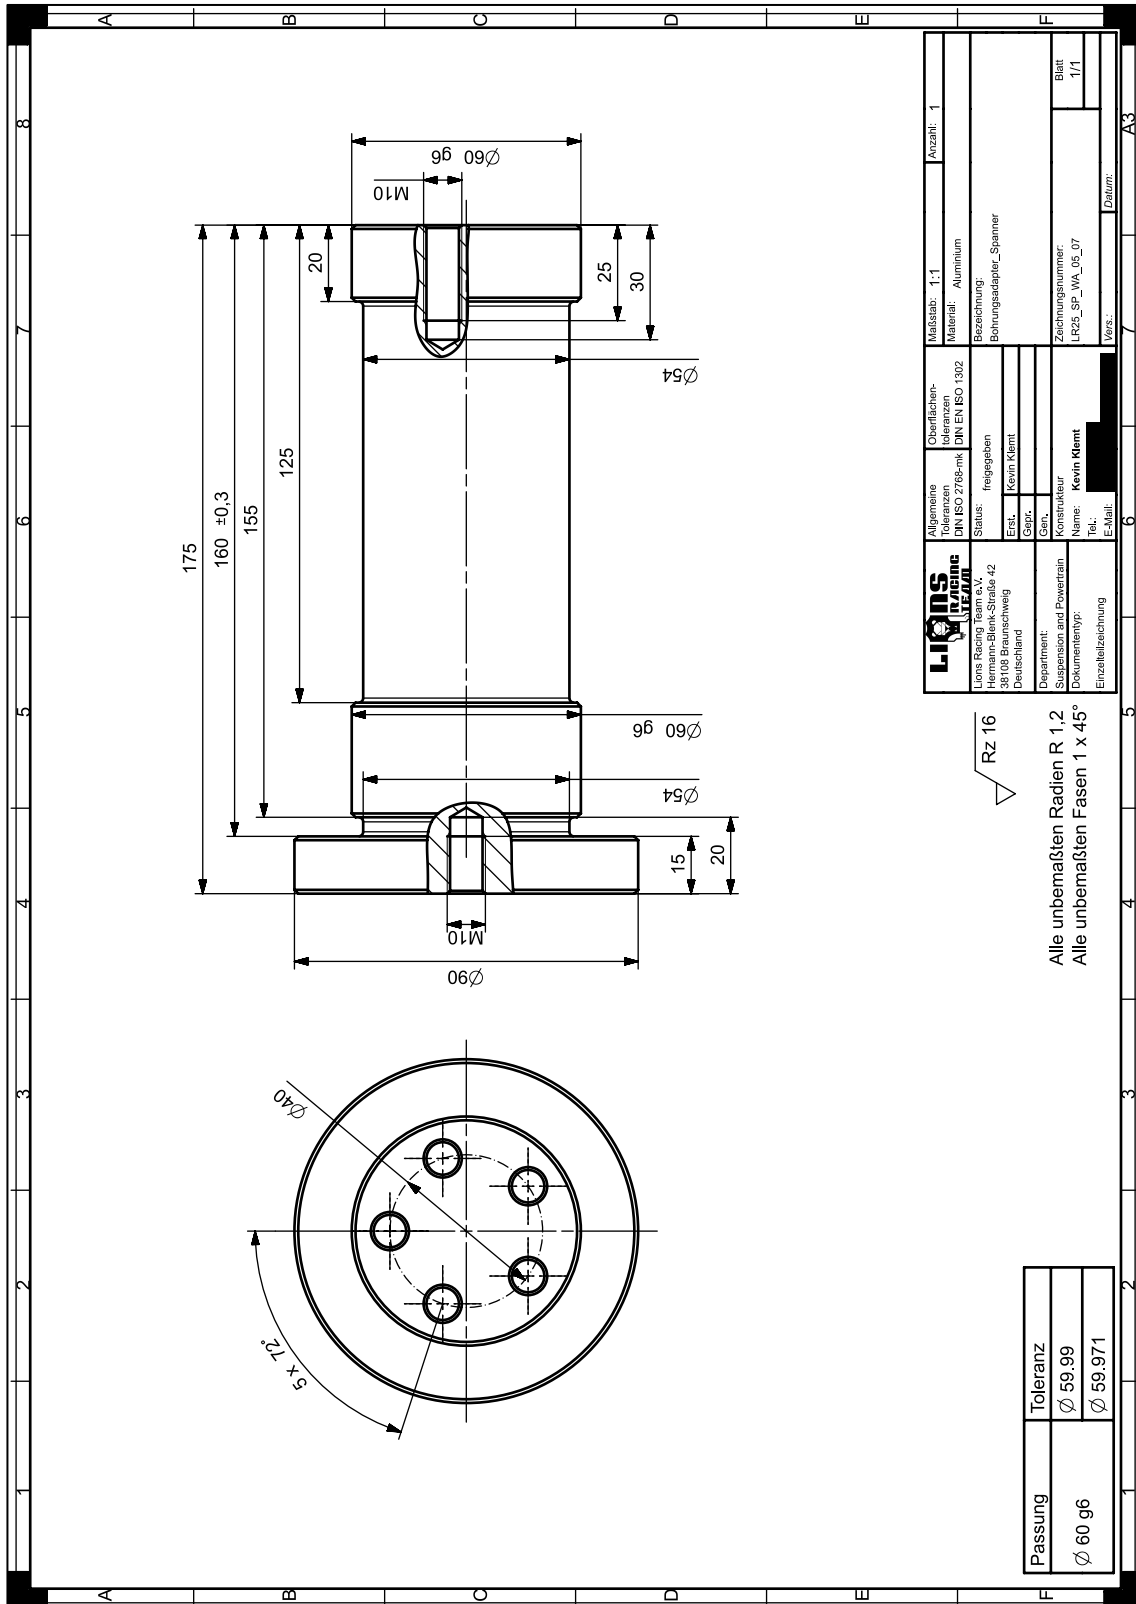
Technische Zeichnung Bohradapter (3/4); Spanner [42]
